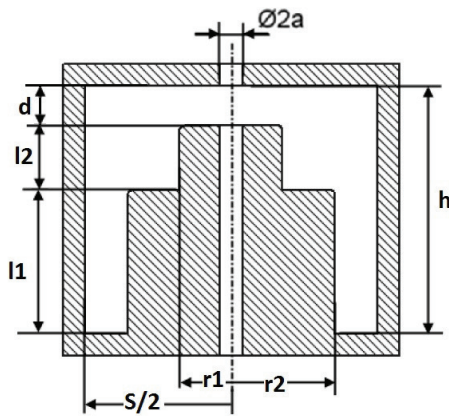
Основные геометрические размеры третьей конструкции резонатора
